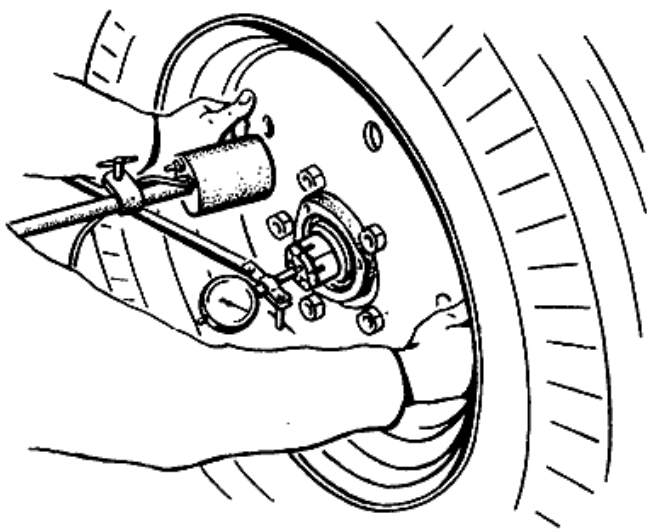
Проверка осевого зазора в подшипниках переднего колеса
